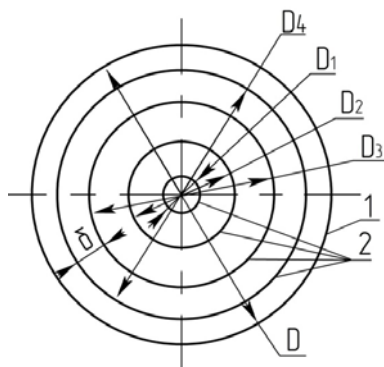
Схема установки рукавов в предлагаемой полезной модели (вид сверху)
